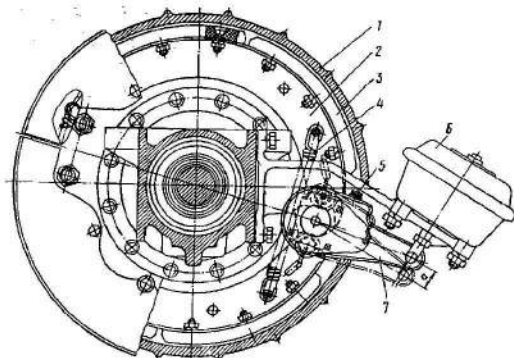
Рабочий тормоз: 1 - тормозной барабан, 2 - колодки тормоза, 3 - накладка, 4 - пружина, 5 - ось червяка; 6 - тормозная камера; 7 - рычаг тормоза; а - ход штока тормозной камеры
